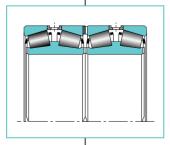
Cuscinetto a sezione leggera tipo LM
